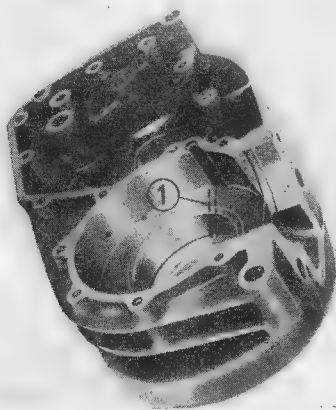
Kontrolle der Ölkanaäle im Gehäuse
